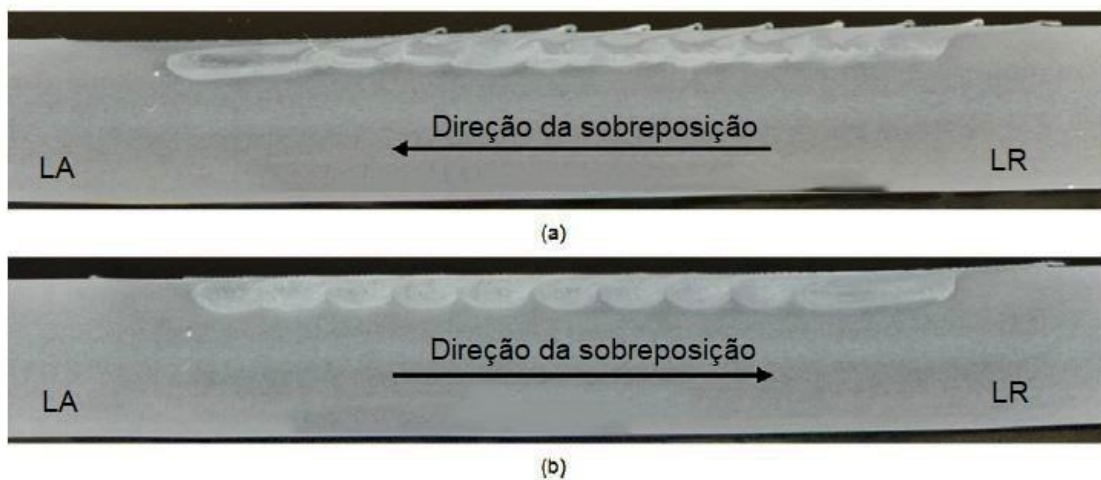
Macrografias de secções de superfícies processadas por fricção linear com sobreposição pelo lado de avanço (a) e lado de retrocesso (b) [26].
